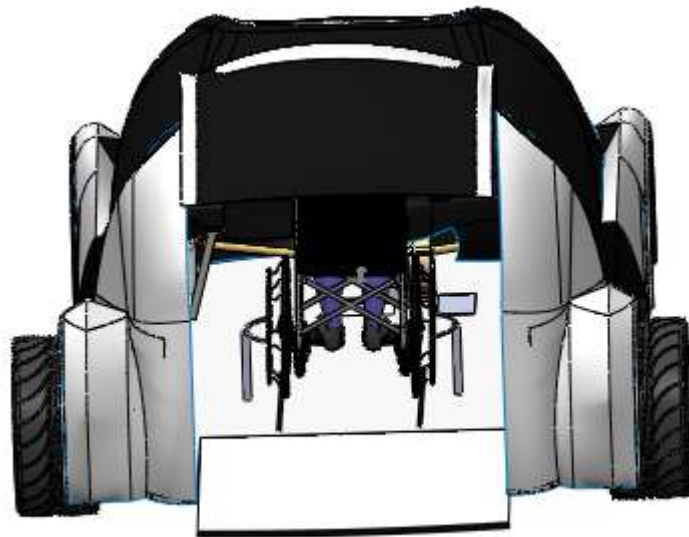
Sistema de apertura de puerta inferior con pistón de elevación. Fuente: (Vaca, José, 2018)
